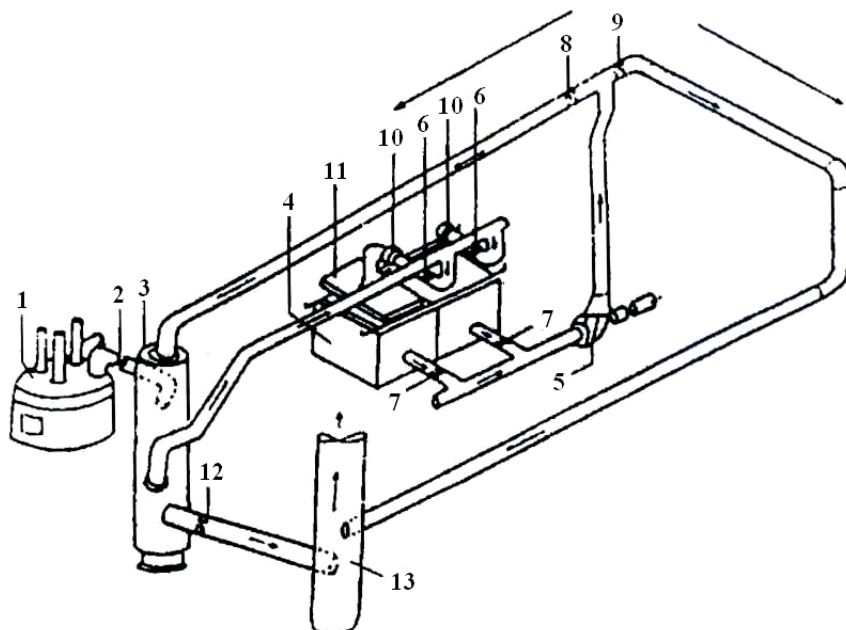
Схема установки предварительного нагрева металлолома:
